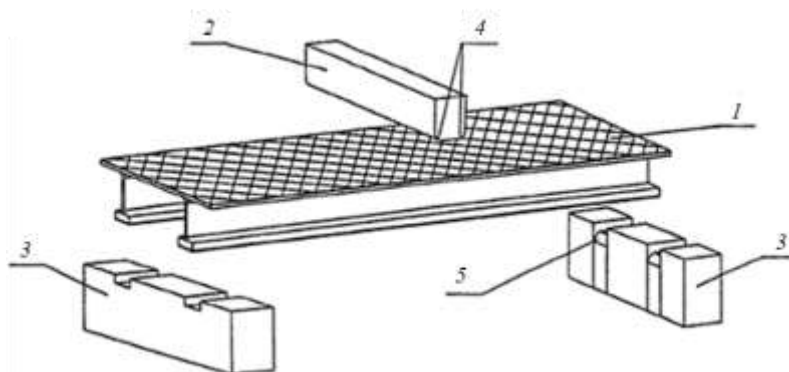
Оснастка для испытаний на трехточечный изгиб КПО сварной гибридной панели крыла: 1 – КПО сварной гибридной панели крыла; 2 – нагружающий наконечник; 3 – опоры со сквозными вырезами; 4 – скругленная контактная поверхность нагружающего наконечника; 5 – скругленная контактная поверхность опоры
